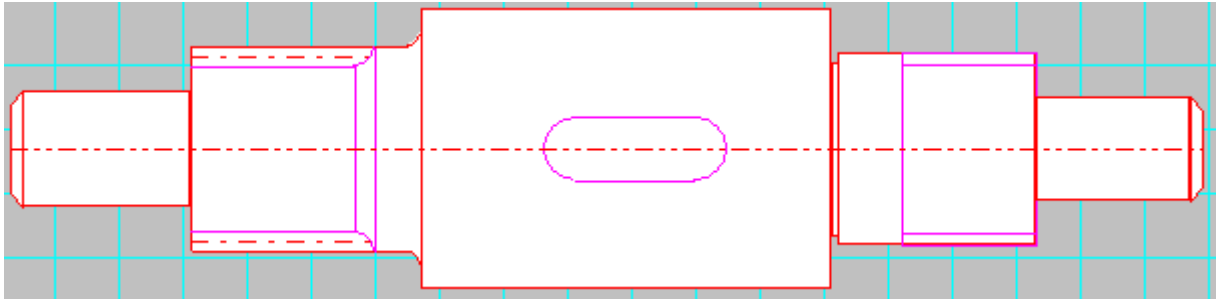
Редактор APM Shaft. Фрагмент вала с резьбой, шпоночным и шлицевым соединением
